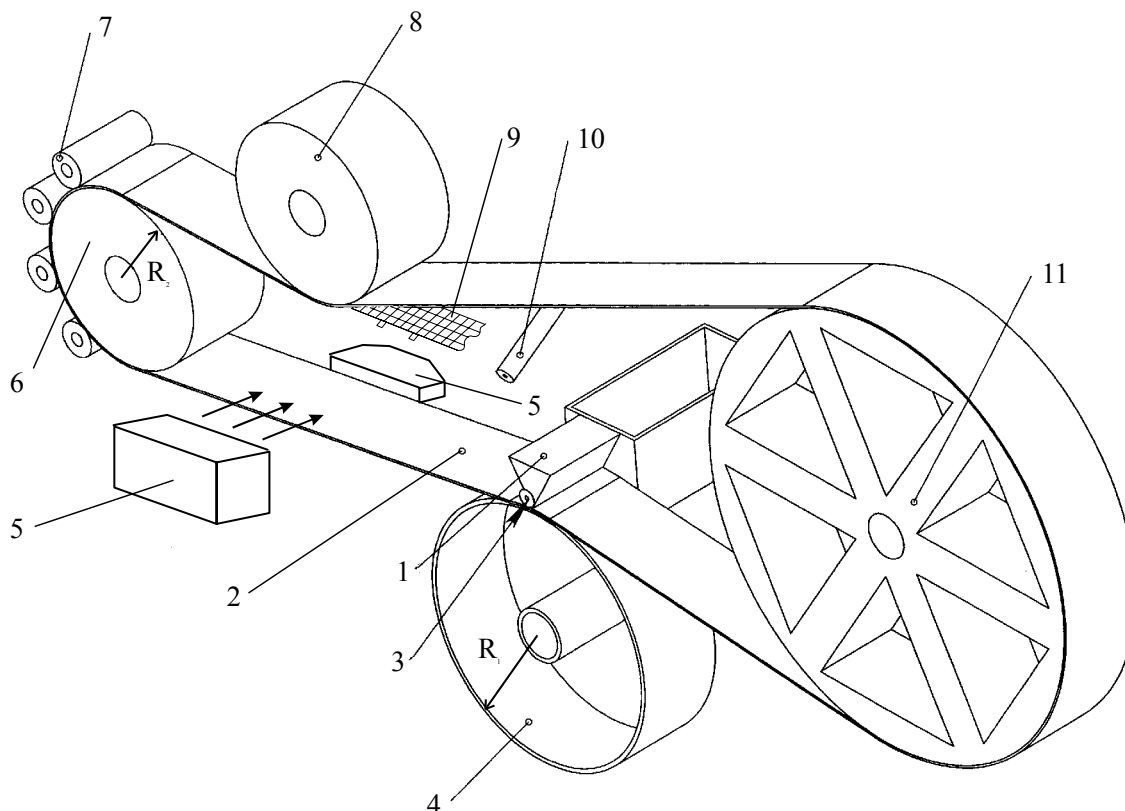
Общая схема непрерывного процесса изготовления токоотводов
